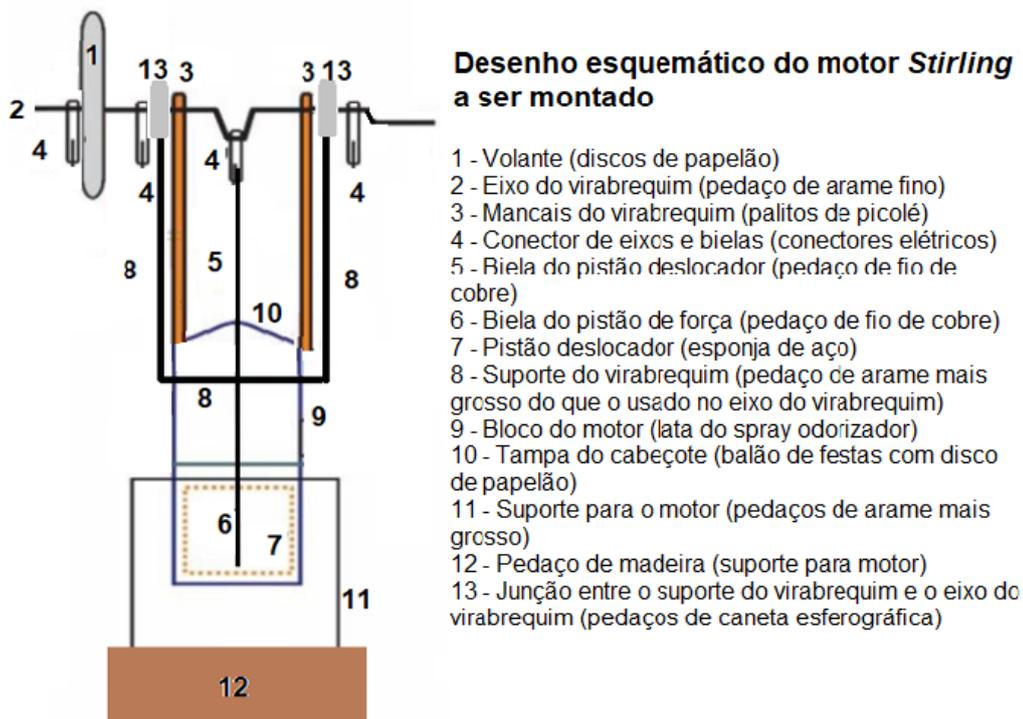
Desenho esquemático do motor *Stirling* a ser montado
